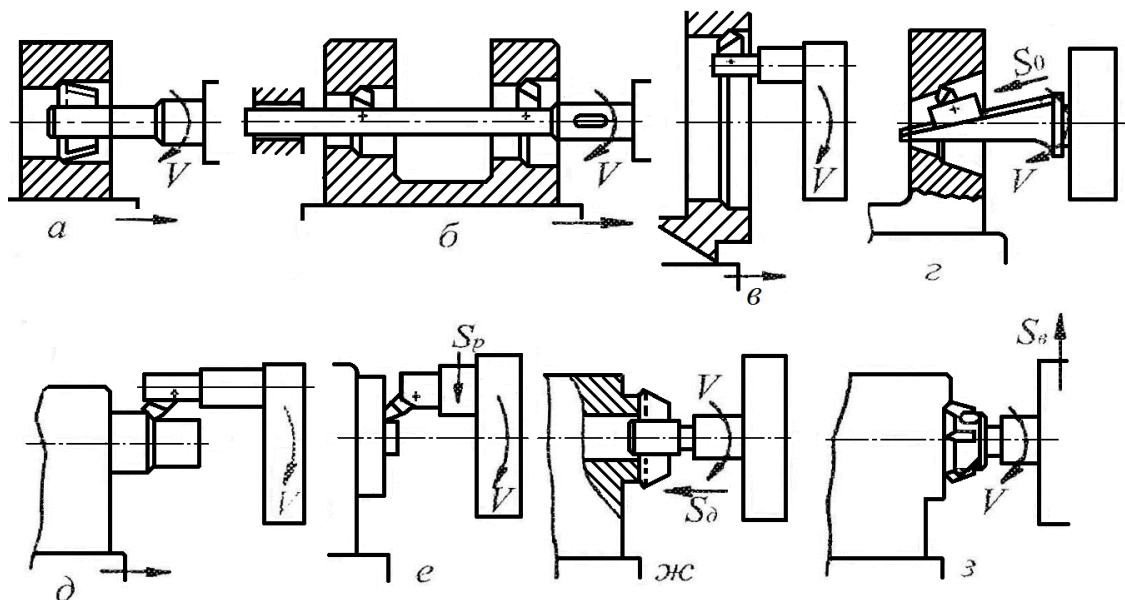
Схеми обробки поверхонь заготовок на горизонтально-розточувальних верстатах
